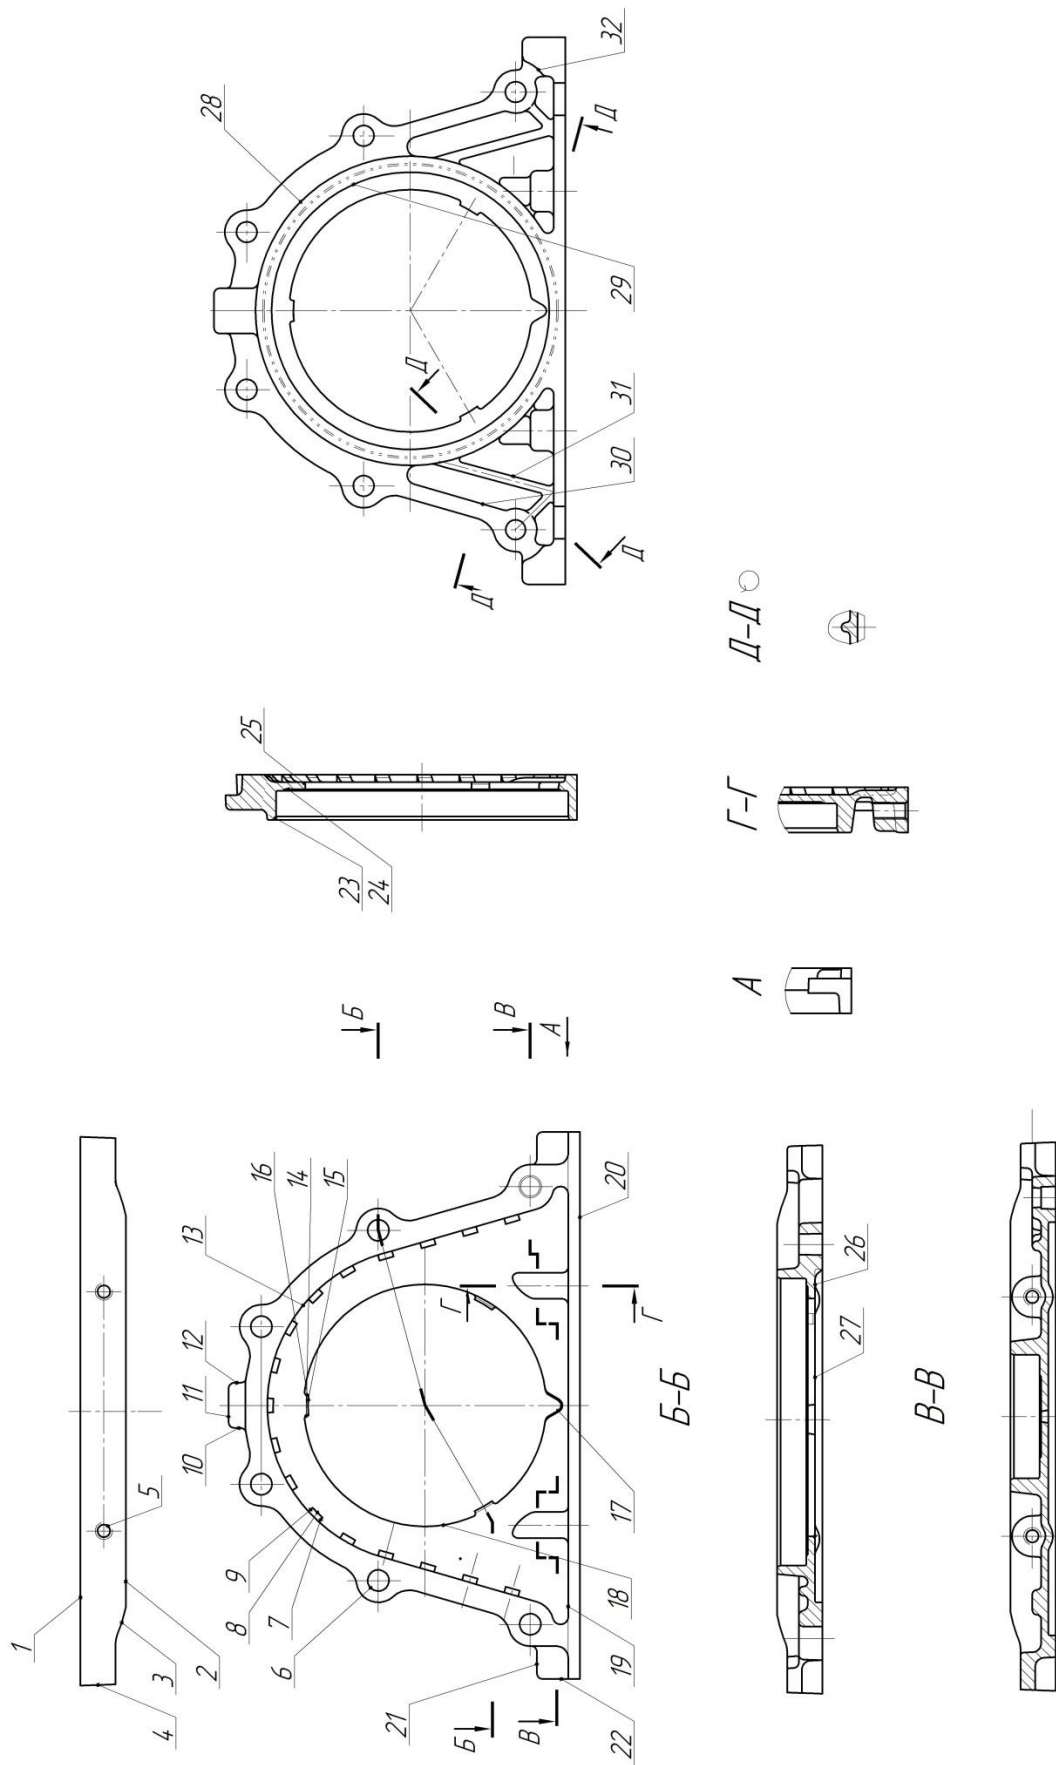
Общий вид детали - «Держатель заднего сальника коленчатого вала»
